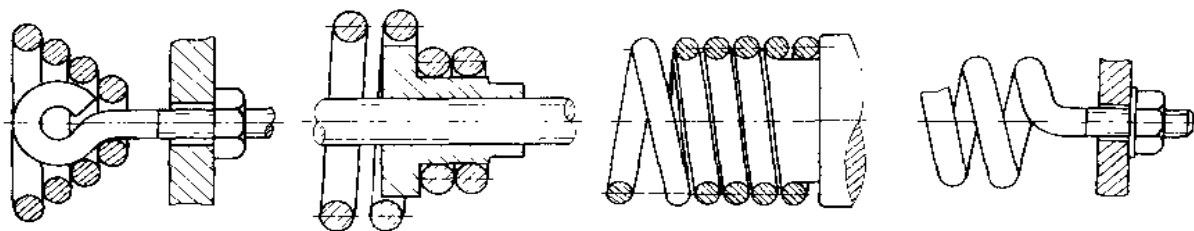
螺杆调整拉力的结构      图 1-7-23 支承座为螺母的调整拉力的结构      图 1-7-24 旋塞式调整结构      图 1-7-25 直尾式调整结构
